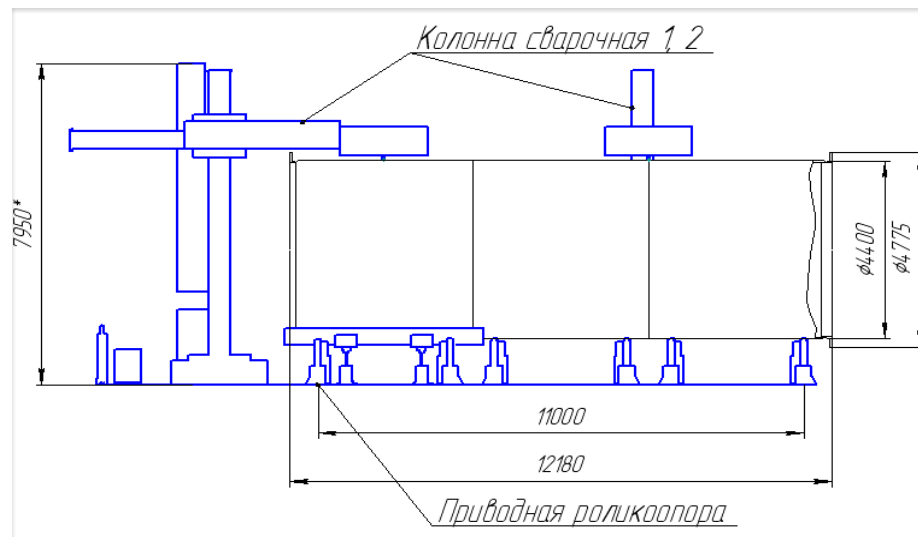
Установка для автоматической сварки в среде защитных газов
